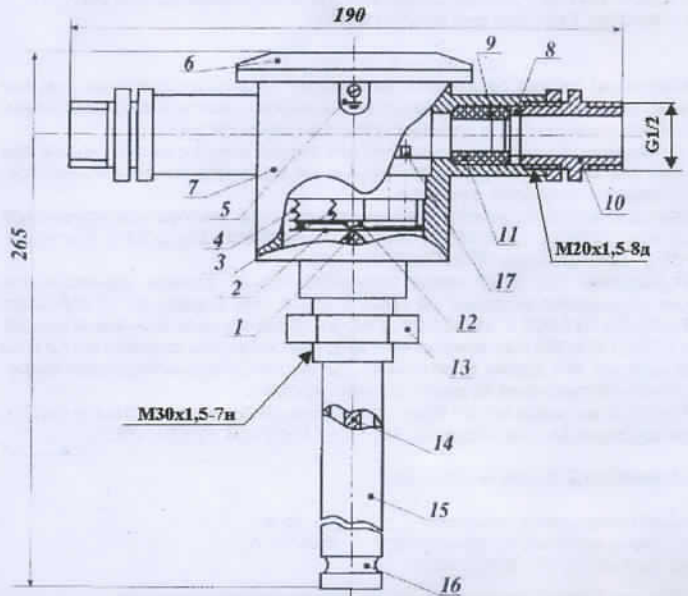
1 - Упор; 2 - Нижняя пружина; 3 - Верхняя пружина; 4 - Пружина сжатия; 5 - Винт заземления; 6 - Крышка; 7 - Корпус; 8 - Шайба; 9 - Втулка; 10 - Штуцер; 11 - Сальниковое уплотнение; 12 - Размыкающая пружина; 13 - Гайка; 14 - Стержень; 15 - Трубка; 16 - Заглушка; 17 - Регулировочный винт.
